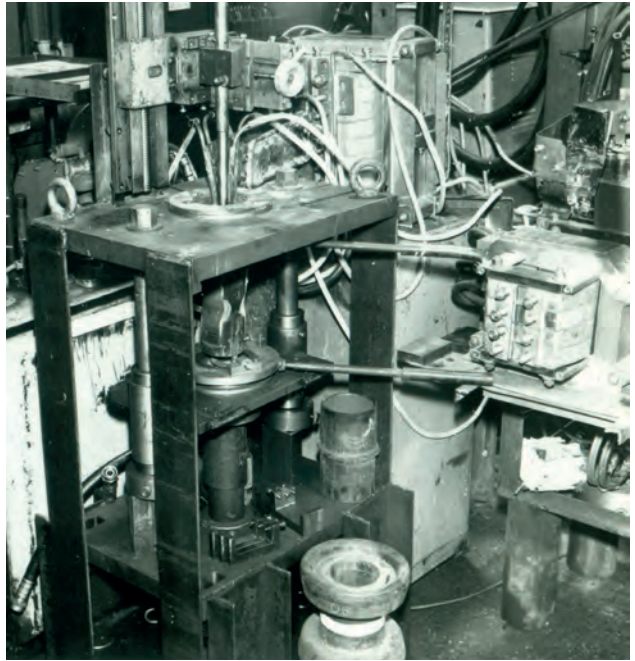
Лабораторна установка індукційного зварювання за допомогою внутрішнього індуктора
